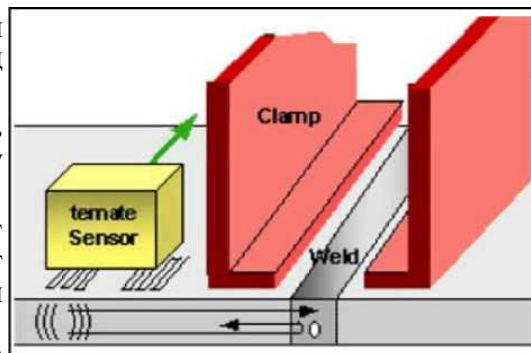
Ультразвуковой метод EMAT контроля сварного шва соединенных колец
